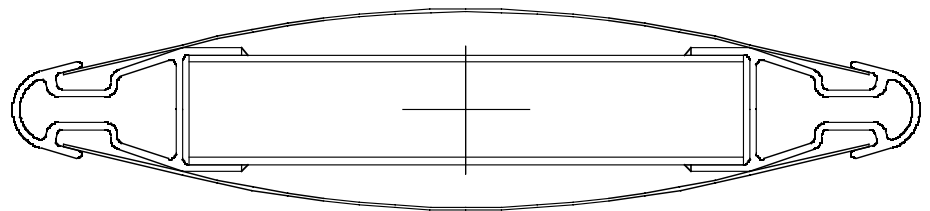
Querschnitt Alu-Lamelle mit Deckschicht aus Aluminiumblech 1,5 mm
